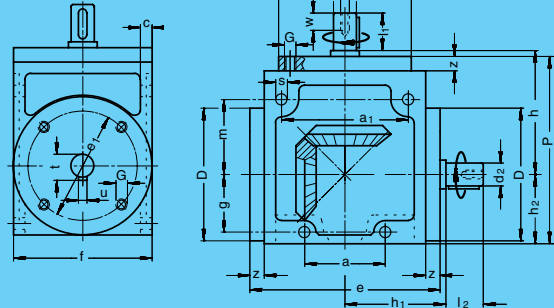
Ausführung mit Gewichtserleichterung, rechts/rechts drehend
